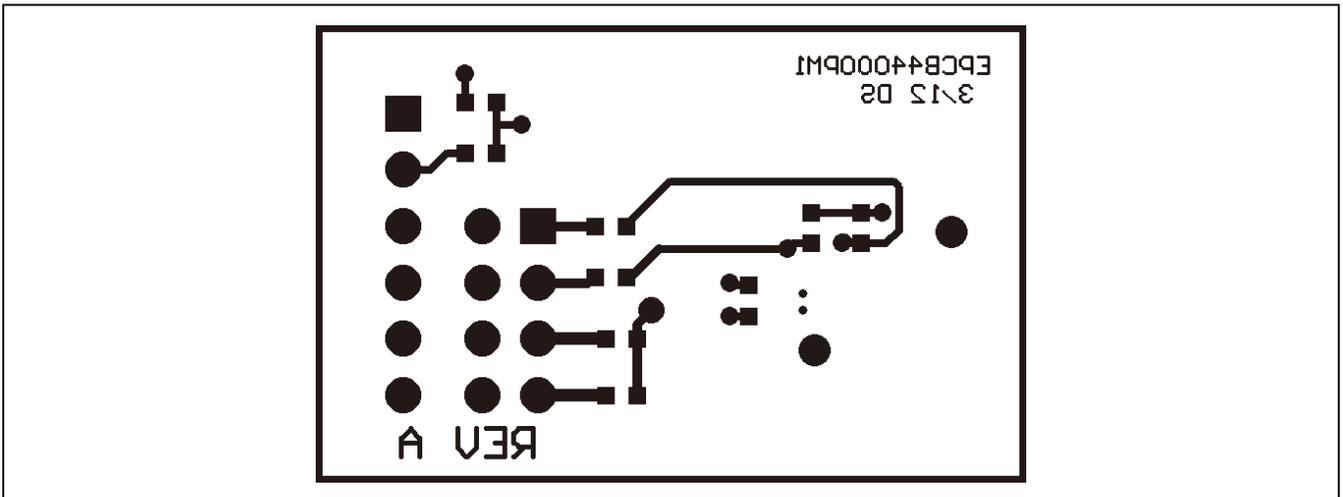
MAX44000PMB11外设模块PCB布局—焊接层
